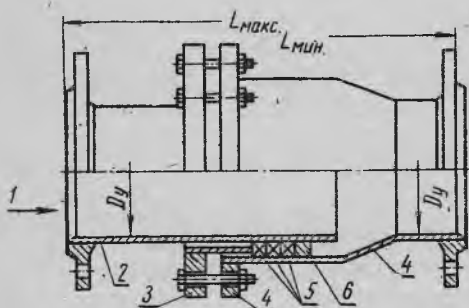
Монтажная вставка сварной конструкции:
